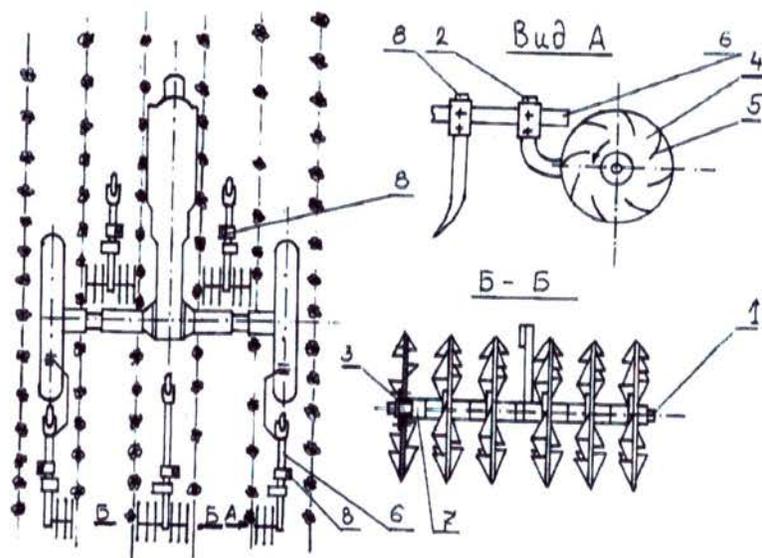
Установка рабочих органов в ряд для разрушения почвенной корки и рыхления середины междурядья:
